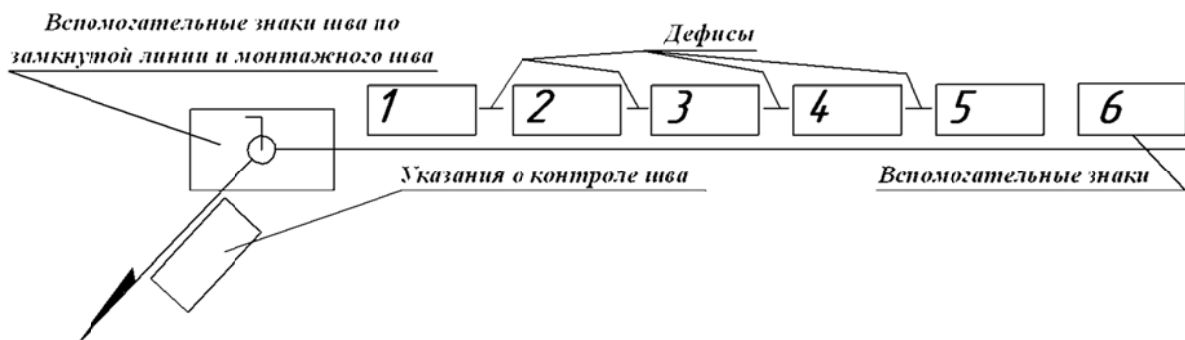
Структура условного обозначения стандартного шва или одиночной сварной точки
